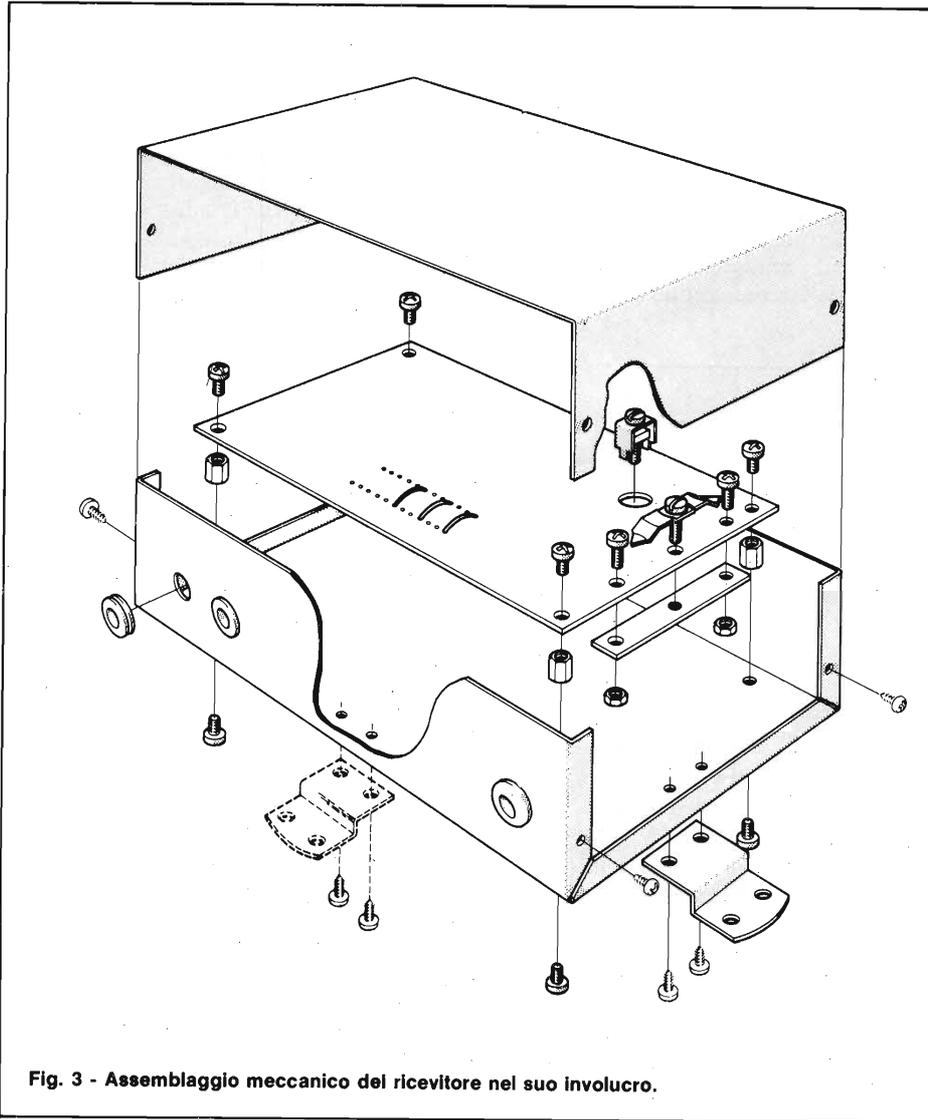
Assemblaggio meccanico del ricevitore nel suo involucro.
